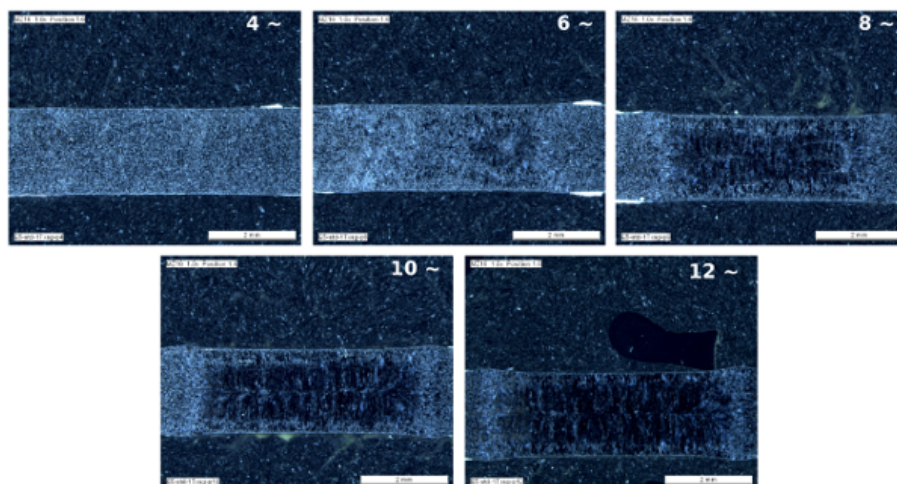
Cinétique expérimentale de développement du noyau - assemblage 1T XSG 2mm - 100 points soudés.
